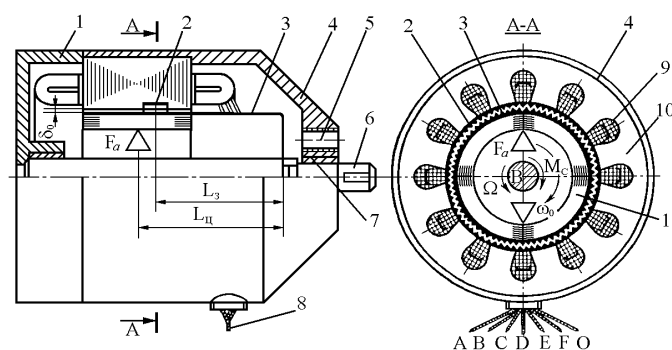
Общий вид респонсина с  $m = 6$ мм: 1 — подшипниковый щит; 2 — круглое жесткое зубчатое колесо (жесткое звено); 3 — упругогибкий ротор с гибким зубчатым венцом (гибкое звено); 4 — корпус машины; 5 — монтажные отверстия; 6 — вал респонсина с узлом крепления ротора; 7 — подшипниковые узлы; 8 — выводные концы обмотки управления; 9 — обмотка управления; 10 — статор ЭМГ; 11 — гибкий магнитопровод ротора
